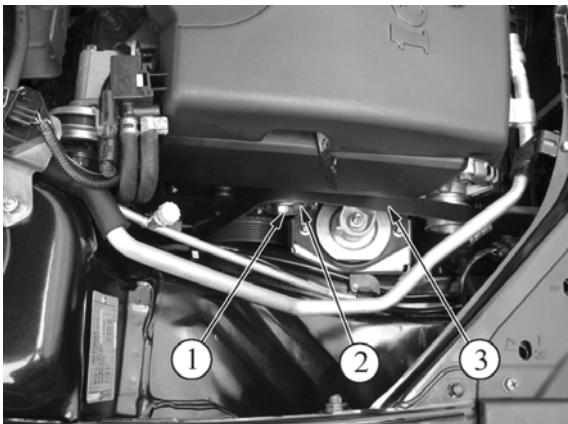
Натяжение ремня привода вспомогательных агрегатов:
